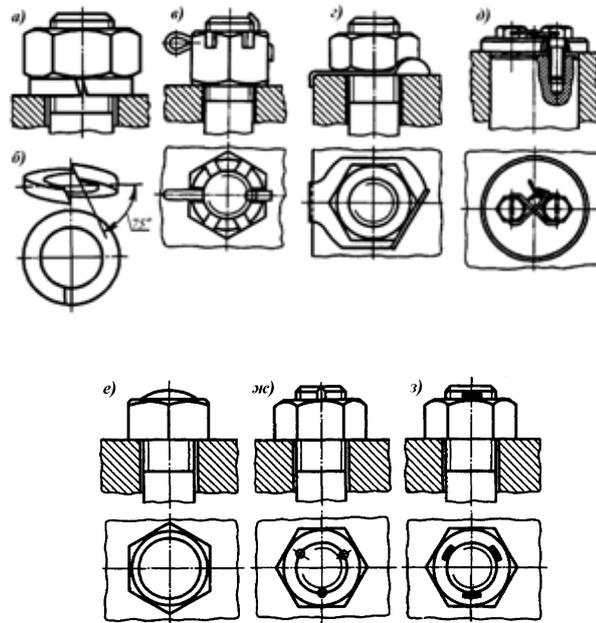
Некоторые способы стопорения резьбовых соединений: а) установкой пружинной шайбы; б) пружинная шайба в свободном состоянии; в) коронная гайка со шплинтом; г) отгибная шайба с усом; д) обвязка болтов проволокой; е) раклёпывание выступающего конца болта; ж) кернение в резьбу; з) прихватка сваркой в резьбу
